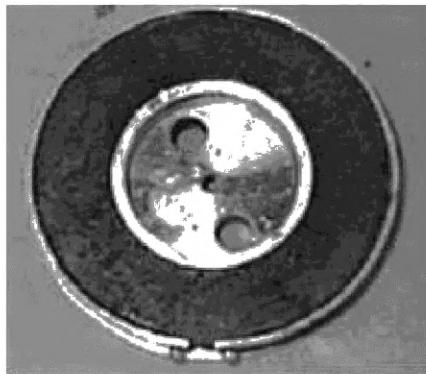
Кольцевая форма в сборе (вид сверху)
